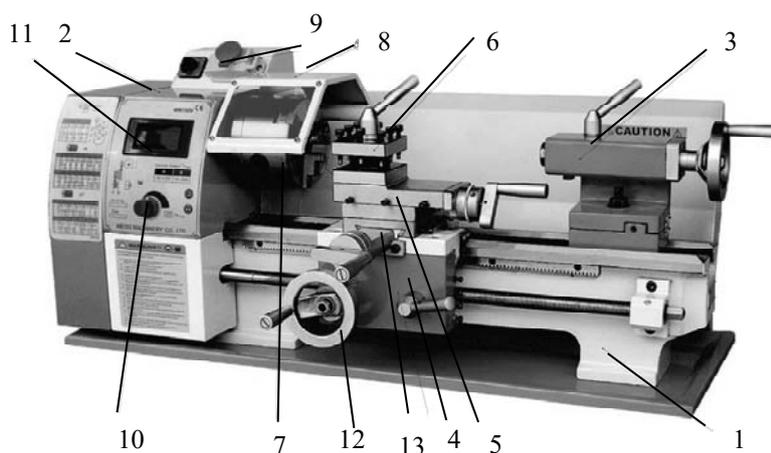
Общий вид токарного настольного станка Universal WM180V
